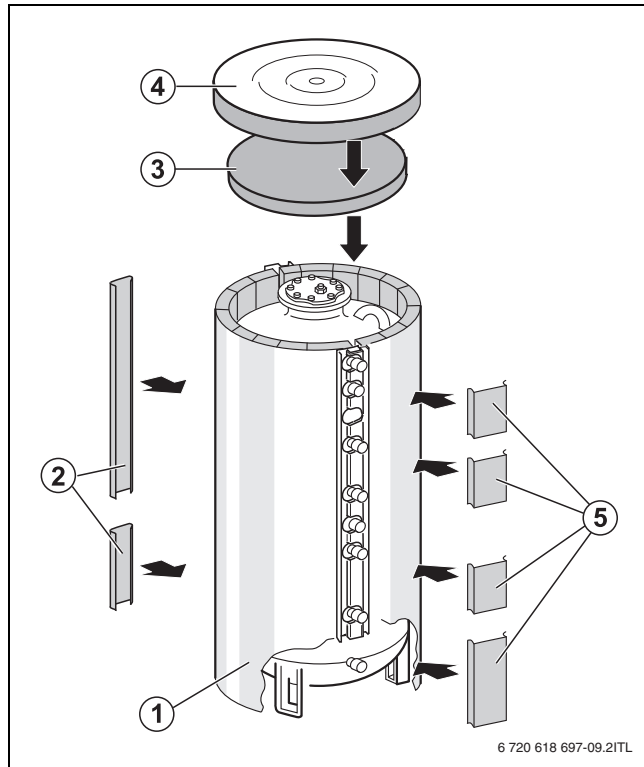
Monter les baguettes de recouvrement et l'isolation thermique supérieure (vue arrière)
